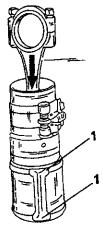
Вдвигать поршень и шатун так, чтобы стороны шатуна совпадали с поверхностями (1) рабочей гильзы цилиндра.
